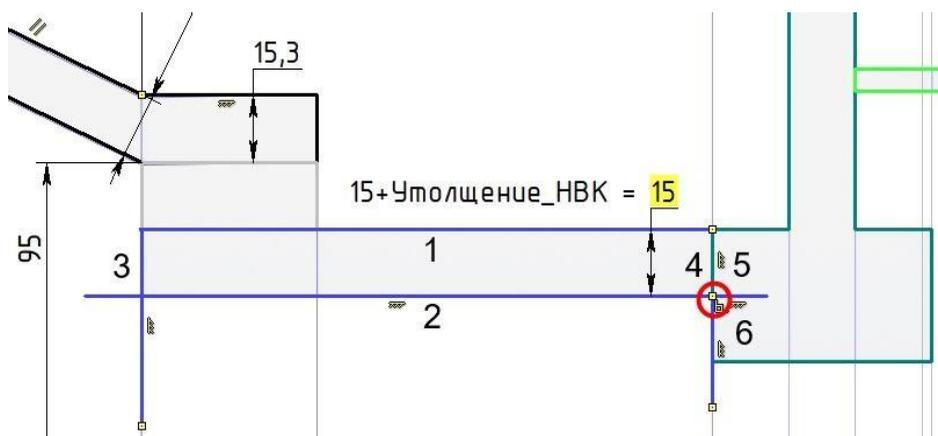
Редактирование 3D-профиля носка вала компрессора
